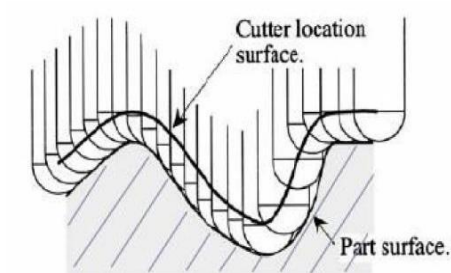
Створення поверхні РР з проєктної поверхні [38]
